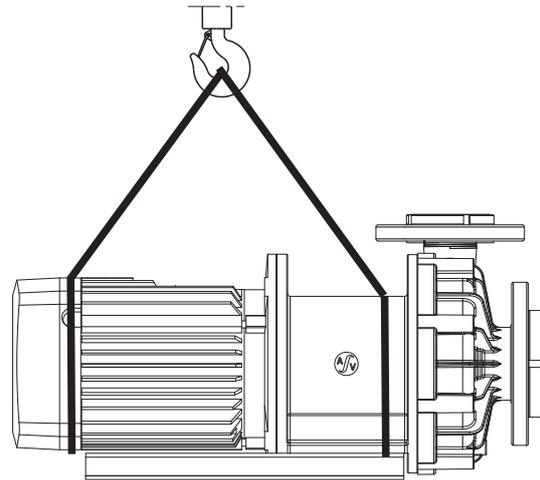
Prinzipskizze: Hebezeug befestigen an Pumpenaggregat
